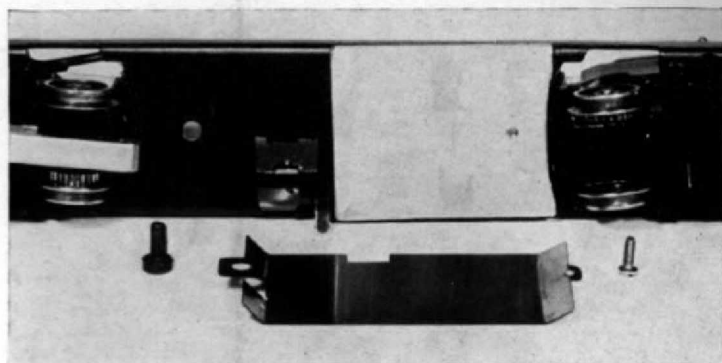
Die beiden Rahmenstücke (s. Abb. 4) werden durch ein 1,5 mm starkes Blech verbunden (verschraubt, siehe Abb. 2). Vorn das neu geformte Abdeckblech, das zusätzlich mit einer 2-mm-Schraube befestigt wird.
